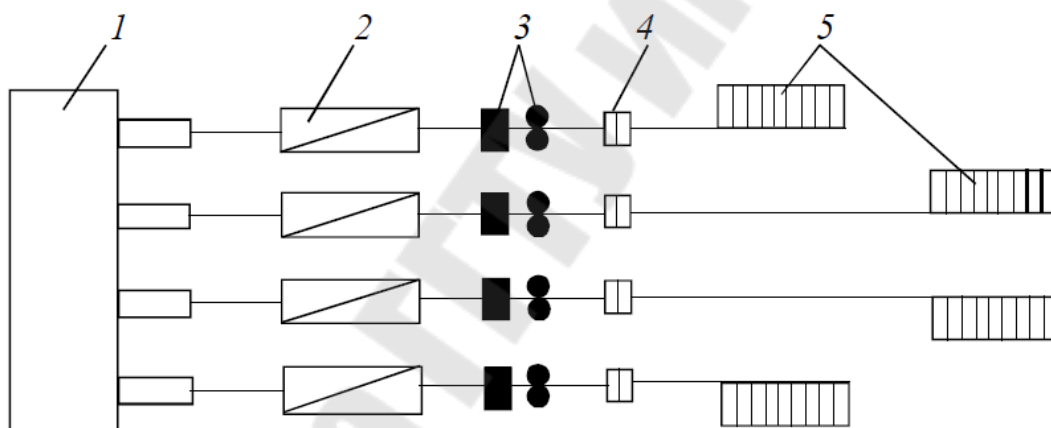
Схема расположения оборудования заготовочного литейно-прокатного агрегата:
